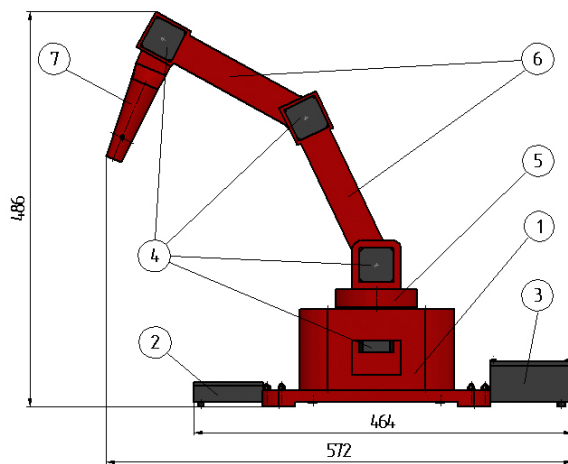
Общий вид опытного образца робота-манипулятора: 1 – основание; 2 – корпус блока управления; 3 – корпус блока питания; 4 – шаговые двигатели; 5 – опорное вращательное звено; 6 – возвратно-поступательные звенья; 7 – захват
